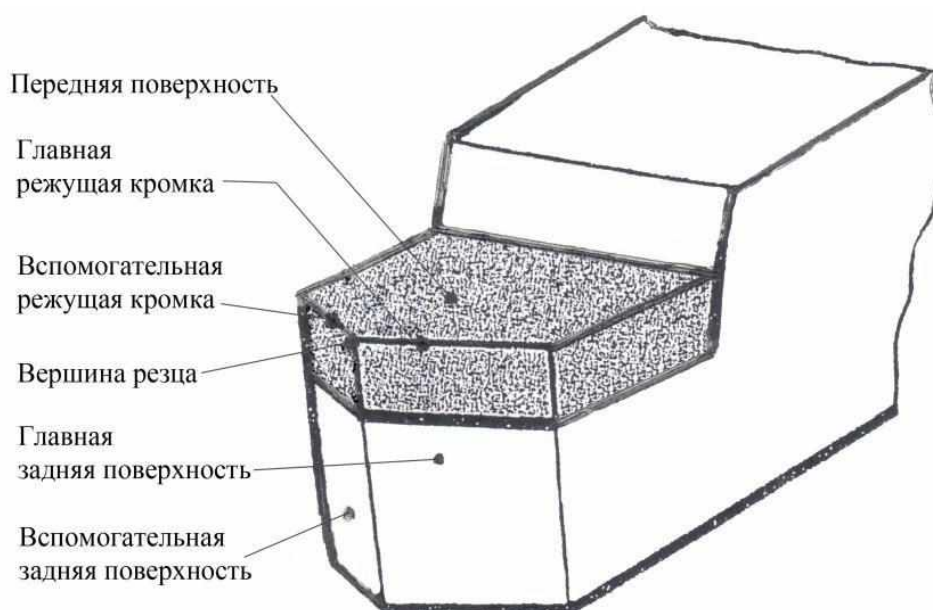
Элементы режущей части прямого проходного резца
